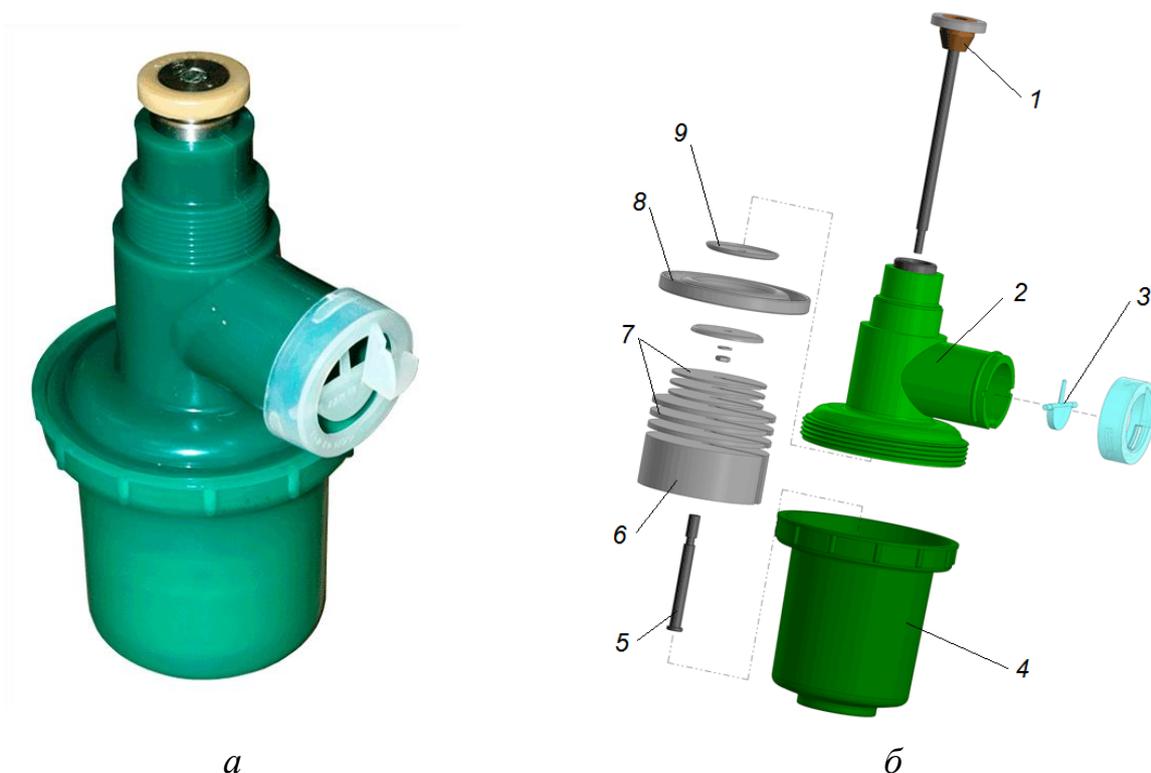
Регулятор тиску вакууму гравітаційного типу: *а* – конструкція; *б* – складові: 1 – клапан; 2 – патрубок-корпус; 3 – показчик потоку; 4 – корпус; 5 – палеці; 6 – вантаж ваговий; 7 – диски вагові додаткові; 8 – гнучка перетинка; 9 – фіксатор перетинки гнучкої.
